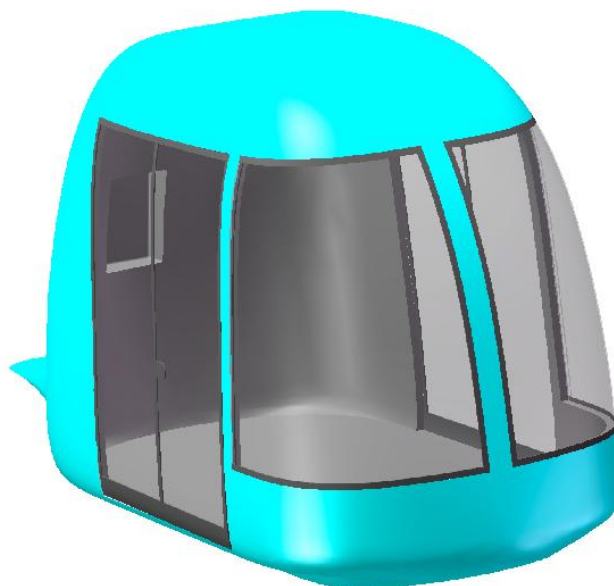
Корпус юнибуса Ю-325П исполнения 01
